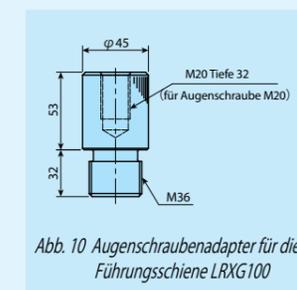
Augenschraubenadapter für die Führungsschiene LRXG100
